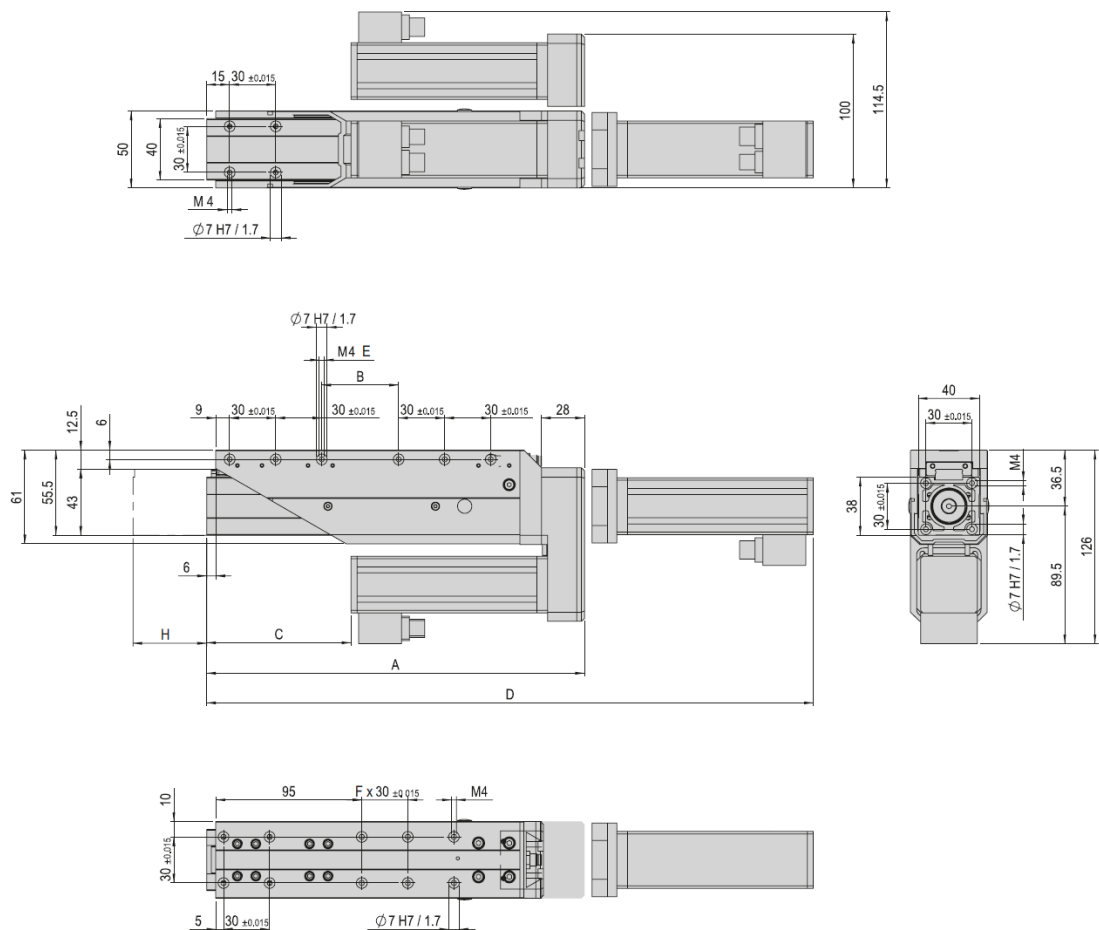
Masszeichnung Spindelausleger SA-3 und SA-3-FL
